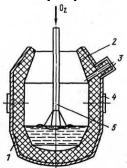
Схема кислородного конвертера: 1 - корпус конвертера, изготовленный из стальных, сваренных встык листов толщиной до 100 мм; 2 - сужающаяся горловина; 3 - сталевыпускное отверстие; 4 – опорный пояс; 5 – кислородная фурма
